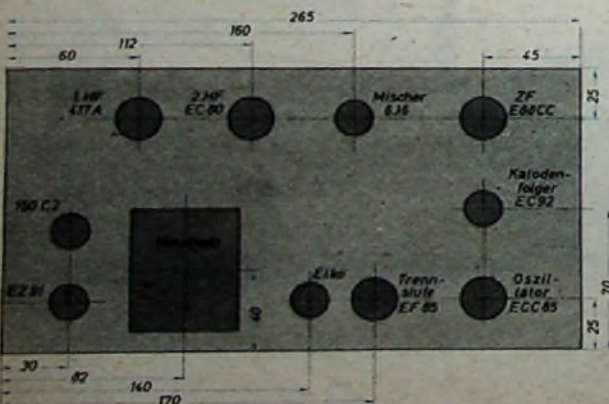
Abmessungen des Chassis und Lage einiger Einzelteile des Konverters
